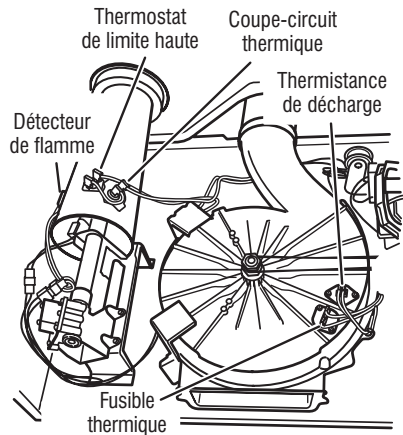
Composants thermiques, sécheuse à gaz, vue de face.
